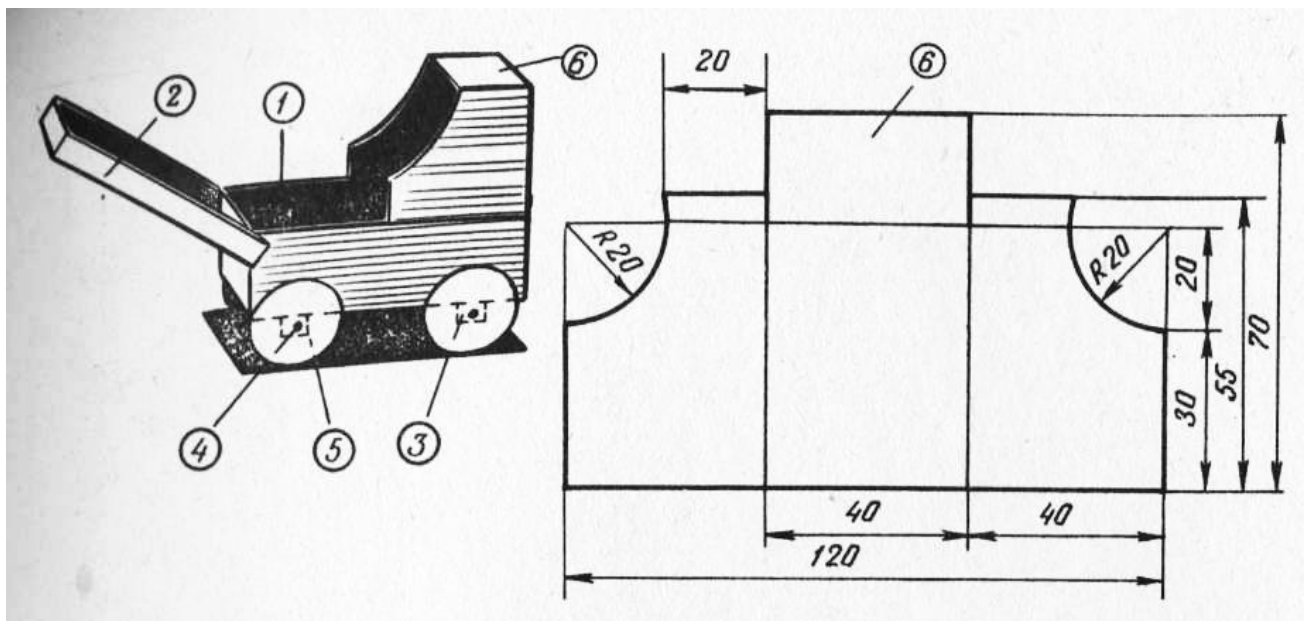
Модель детской коляски: 1— корпус; 2— ручка; 3 — подшипник; 4— ось; 5— колесо; 6— тенд
